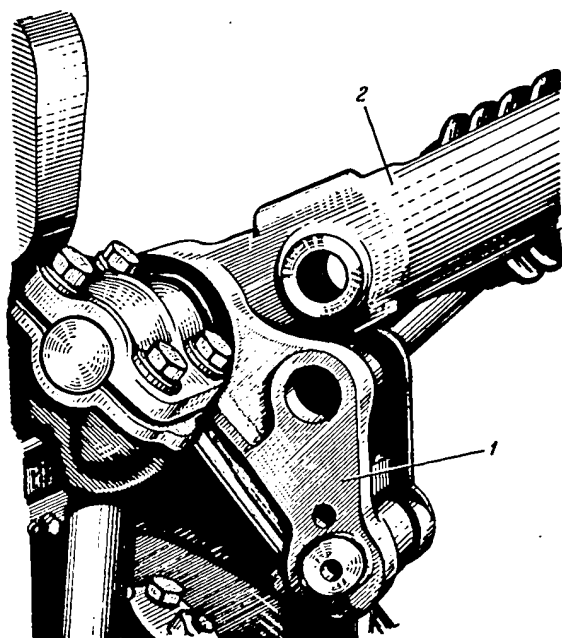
Свободное соединение механизма навески с гидроцилиндром
